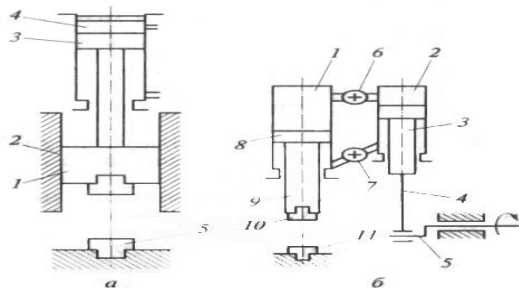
Принципиальные схемы молотов: а - паровоздушного: 1 - баба; 2 - направляющие; 3 - поршень; 4 - цилиндр для подачи пара; 5 - нижний боек; б - пневматического: 1 - рабочий цилиндр; 2 - компрессорный цилиндр; 3 - поршень компрессорного цилиндра; 4 - шатун; 5 - вал; 6, 7 - верхний и нижний золотник соответственно; 8 - поршень рабочего цилиндра; 9 - баба молота; 10 - верхний боек; 11 - нижний боек
